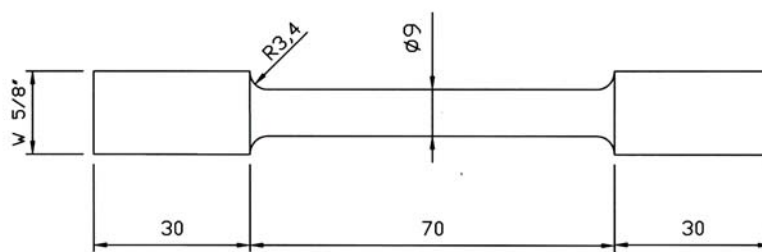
Corpo de prova usinado conforme ASTM A 897M.
